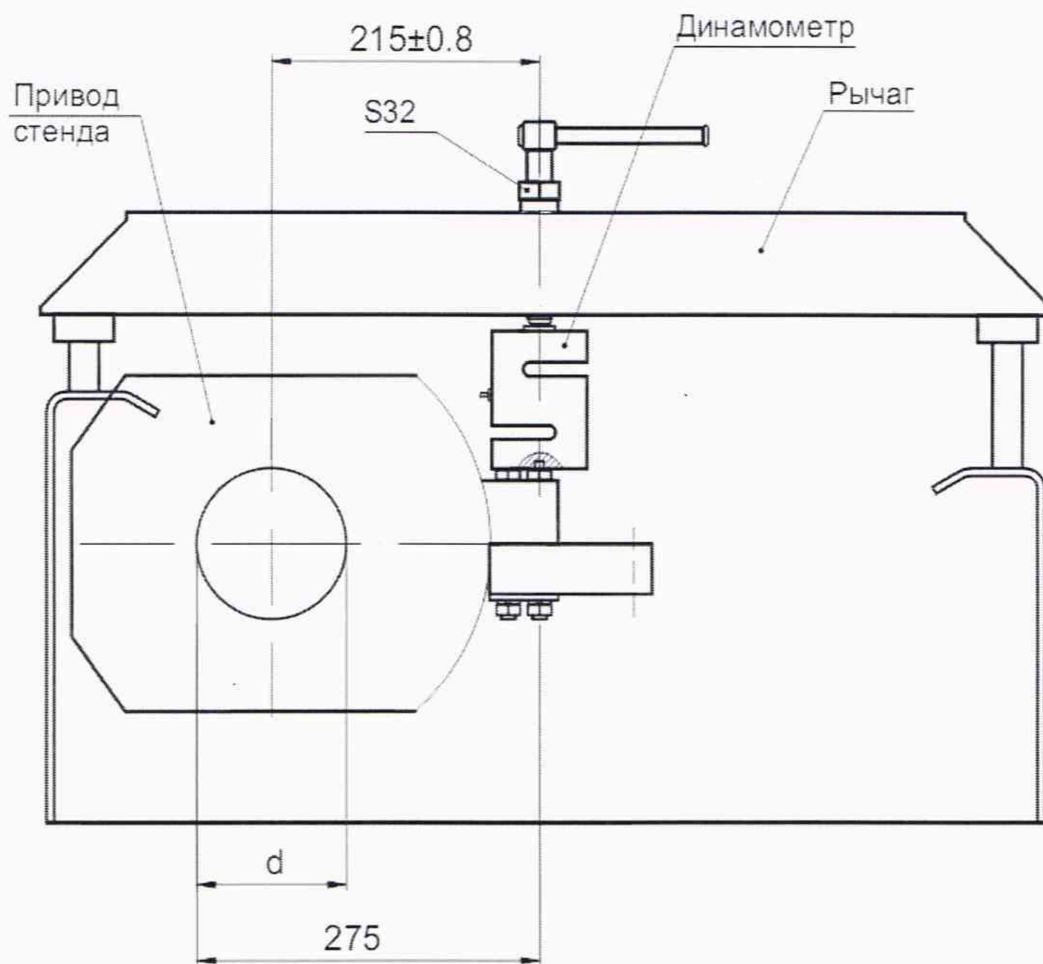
Чертеж рычага М 059.020.00.00-01
